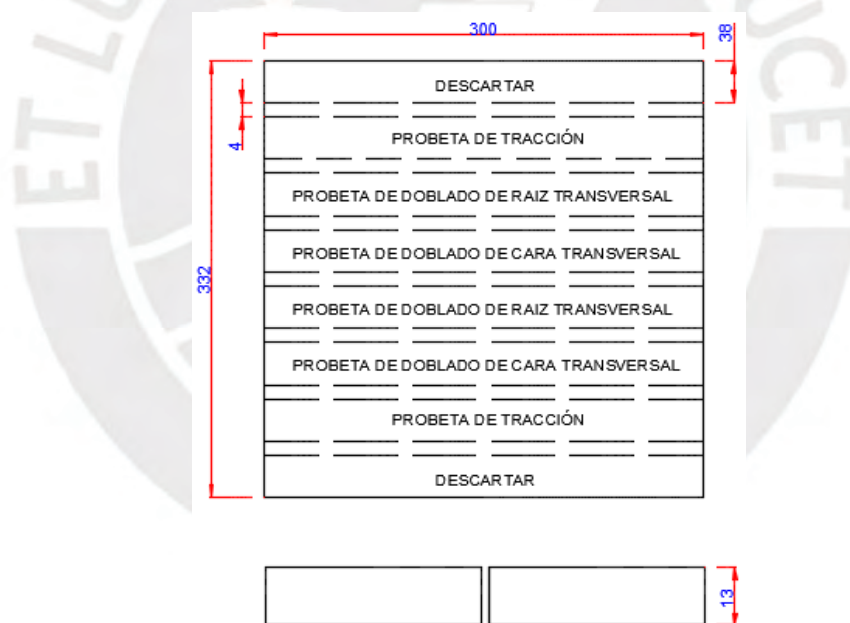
Cupón para calificación de soldadura-WPS N° 204
